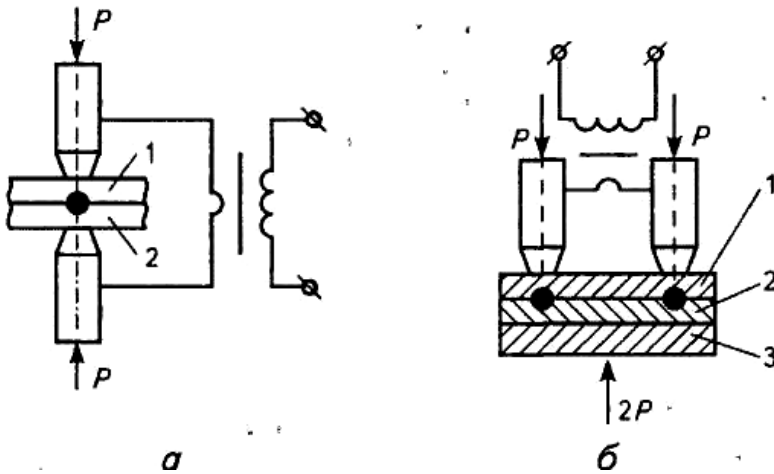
Схеми дво- (а) та одностороннього (б) точкового зварювання
